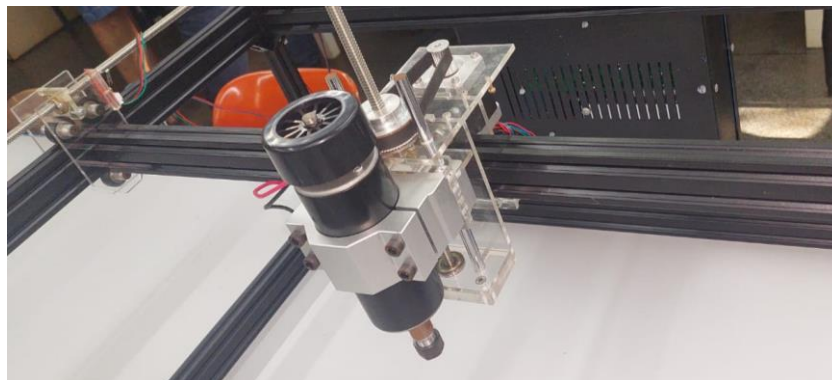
Motor Spindle 500w Er11 CNC Router Fonte CA110/220V
